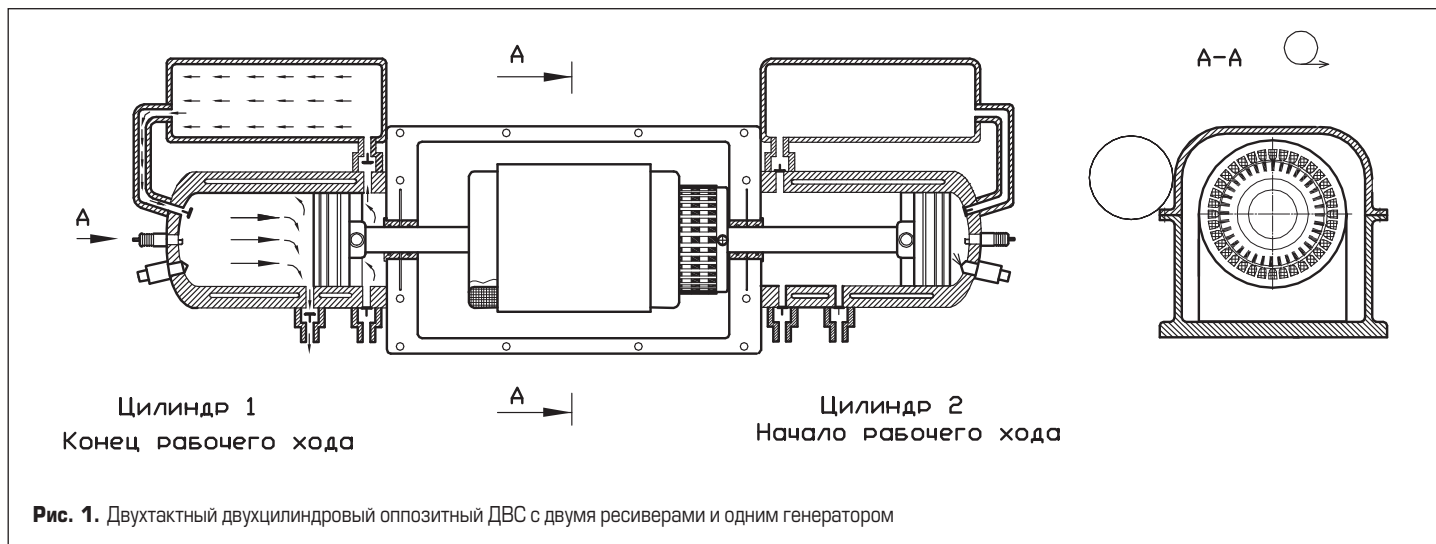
Двухтактный двухцилиндровый оппозитный ДВС с двумя ресиверами и одним генератором
